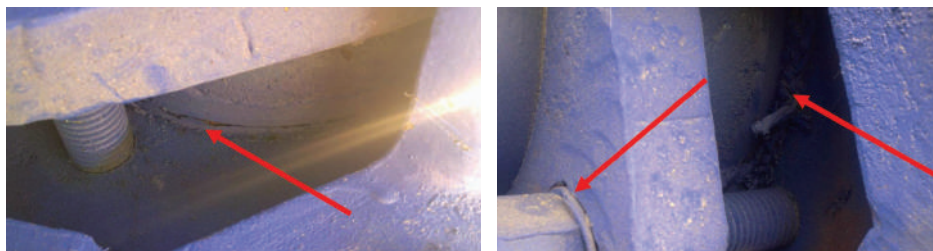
Низкое качество сварки — очень тревожный сигнал
